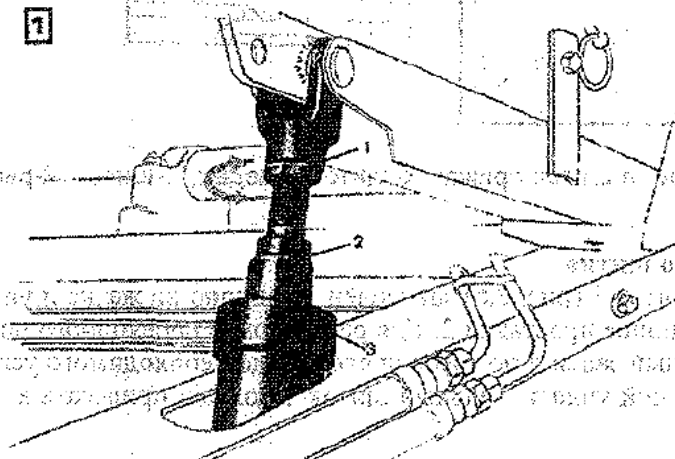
Схема установки мотовила по высоте: 1 – контргайка; 2 – шток; 3 – гидроцилиндр
